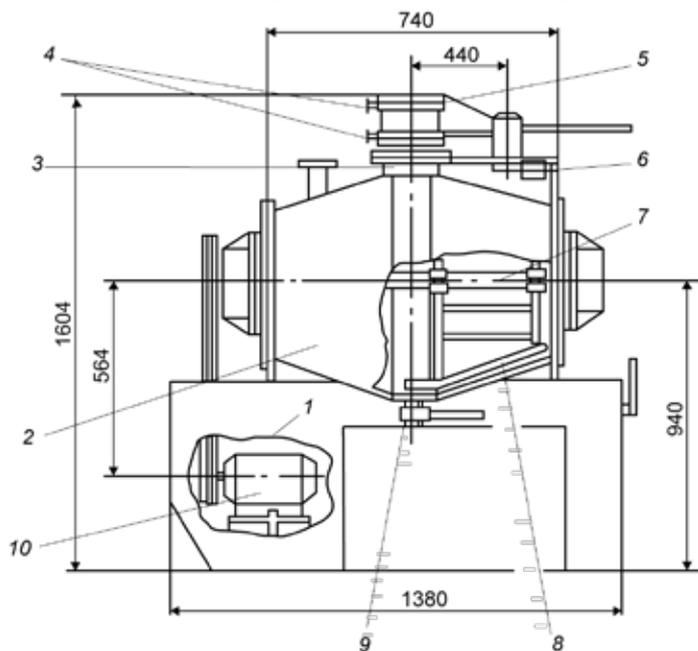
Взбивальная машина ХВА для приготовления теста под давлением
